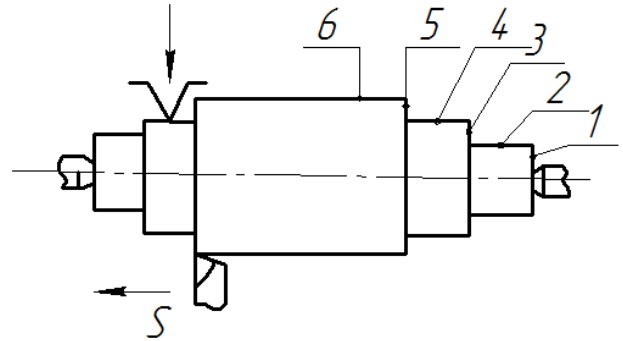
Обробка трьох уступів вала одним різцем за три переходи
